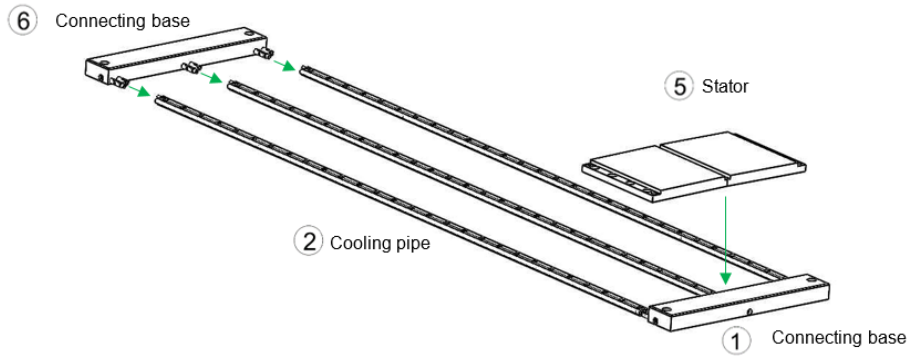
Widok po zamontowaniu układu precyzyjnego chłodzenia forcera wodą
